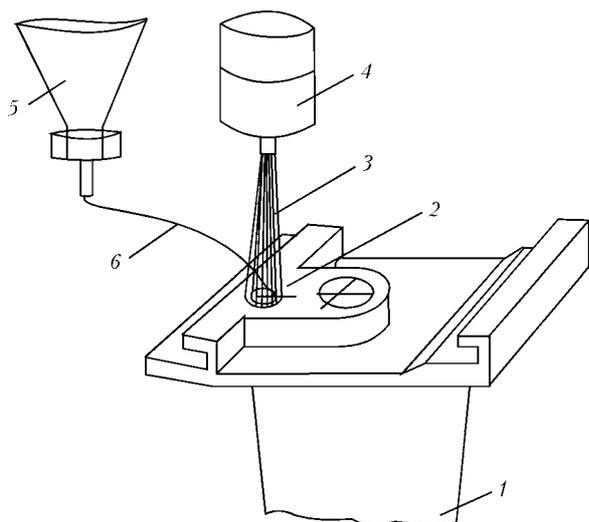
Схема процесса дуговой пайки отверстия под штифт лопатки соплового агрегата ГТД-30КУ: 1 — лопатка; 2 — отверстие под штифт; 3 — дуговой разряд; 4 — горелка; 5 — питатель для подачи порошкового припоя; 6 — транспортирующая труба
